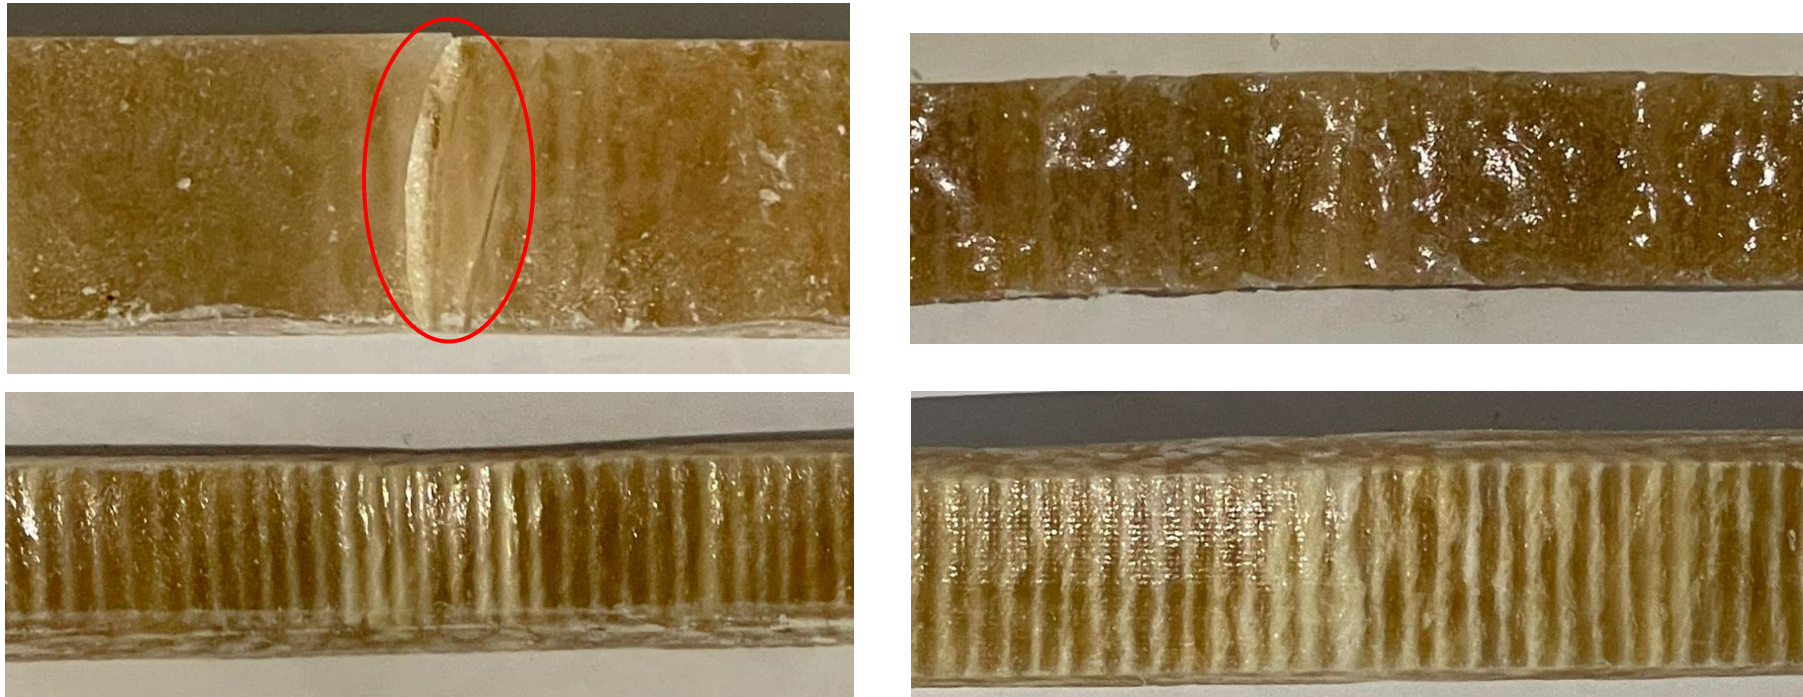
faciès de rupture des éprouvettes sous forme concave (Eprouvette 1), convexe (Eprouvette 3).
